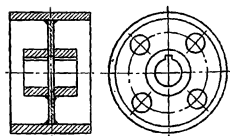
Ротор синхронной машины в виде сварного магнитного колеса.
